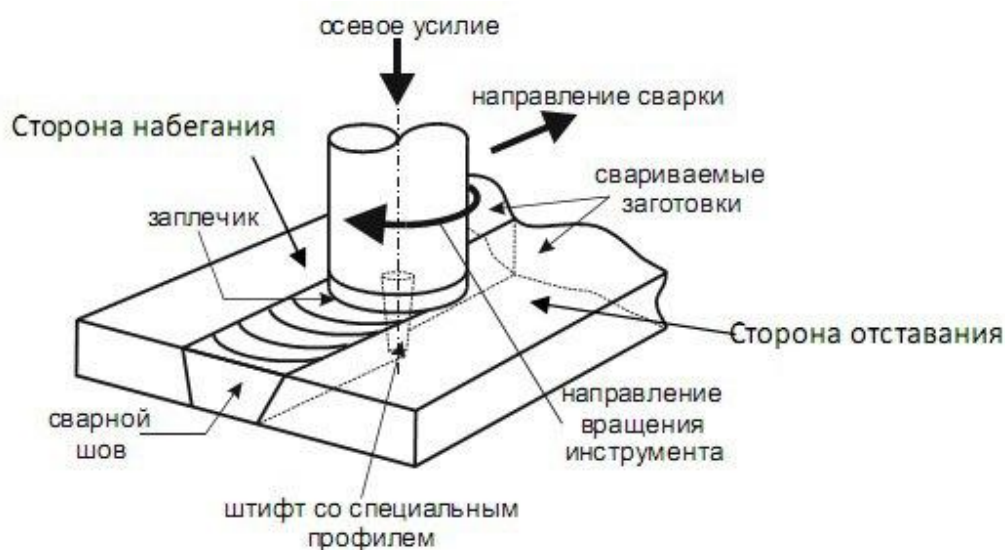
Схема процесса сварки трением с перемешиванием
